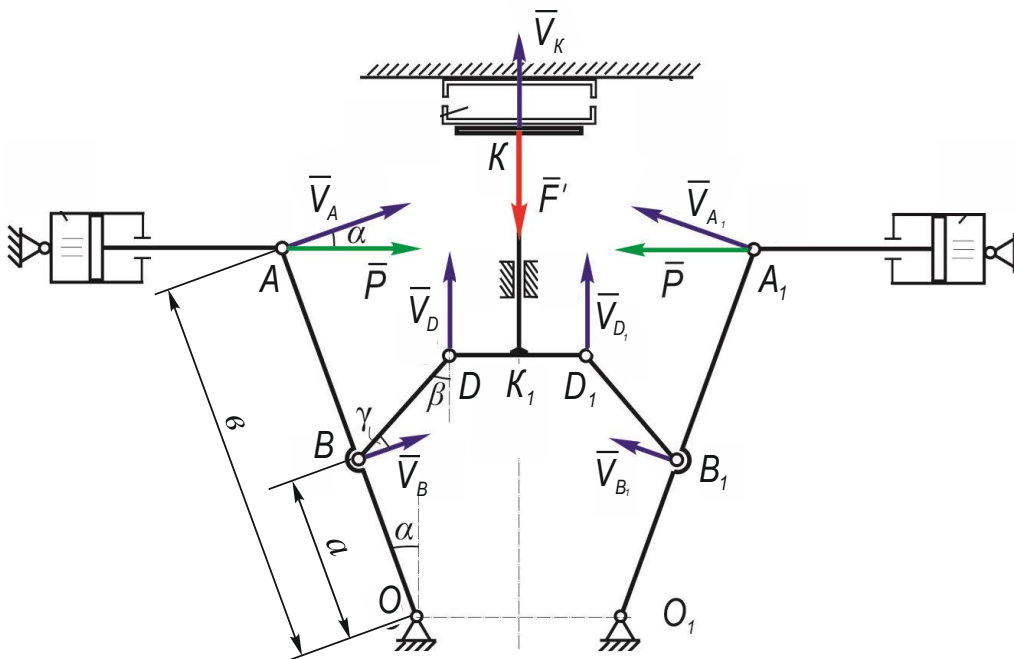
Схема затискувача пакету в машині для зварювання профілів
